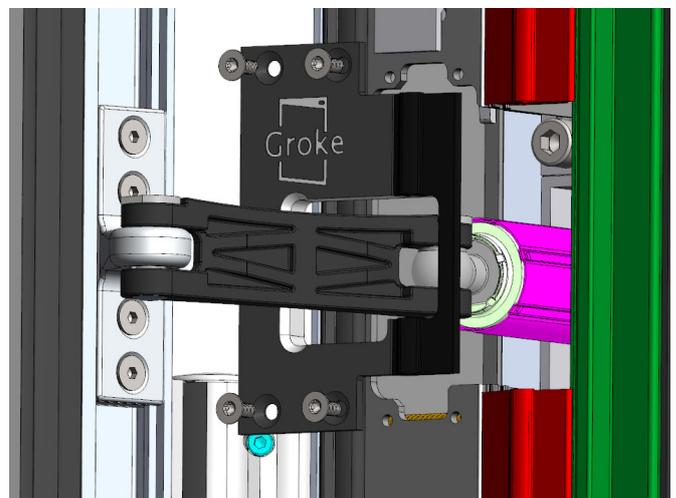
Befestigungsschrauben des Haltewinkels (4 Stück Innensechskant SW 4 mm; Anzugsmoment: 3 Nm)
